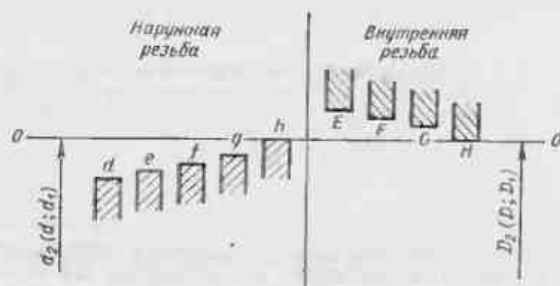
Схемы полей допусков для метрической резьбы с зазором
